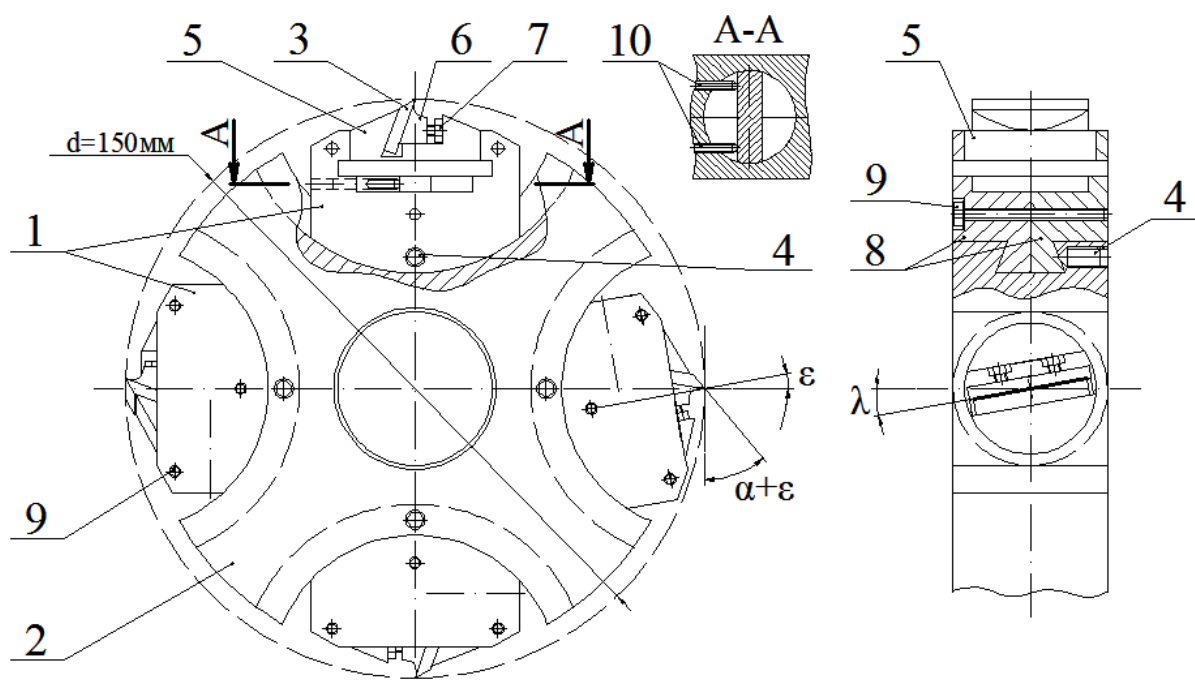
Конструкция сборной фрезы с изменяемыми угловыми параметрами
